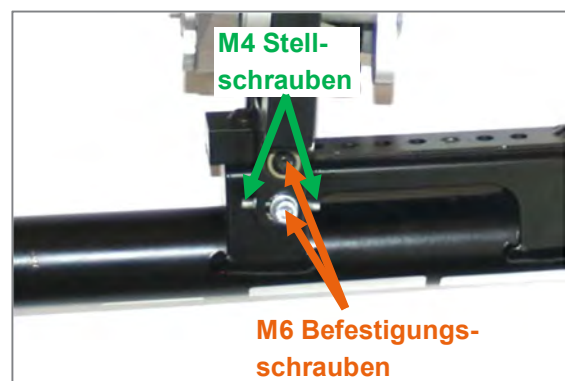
M6 Befestigungsschrauben und M4 Stellschrauben zur Winkelverstellung der Verriegelungsplatte
